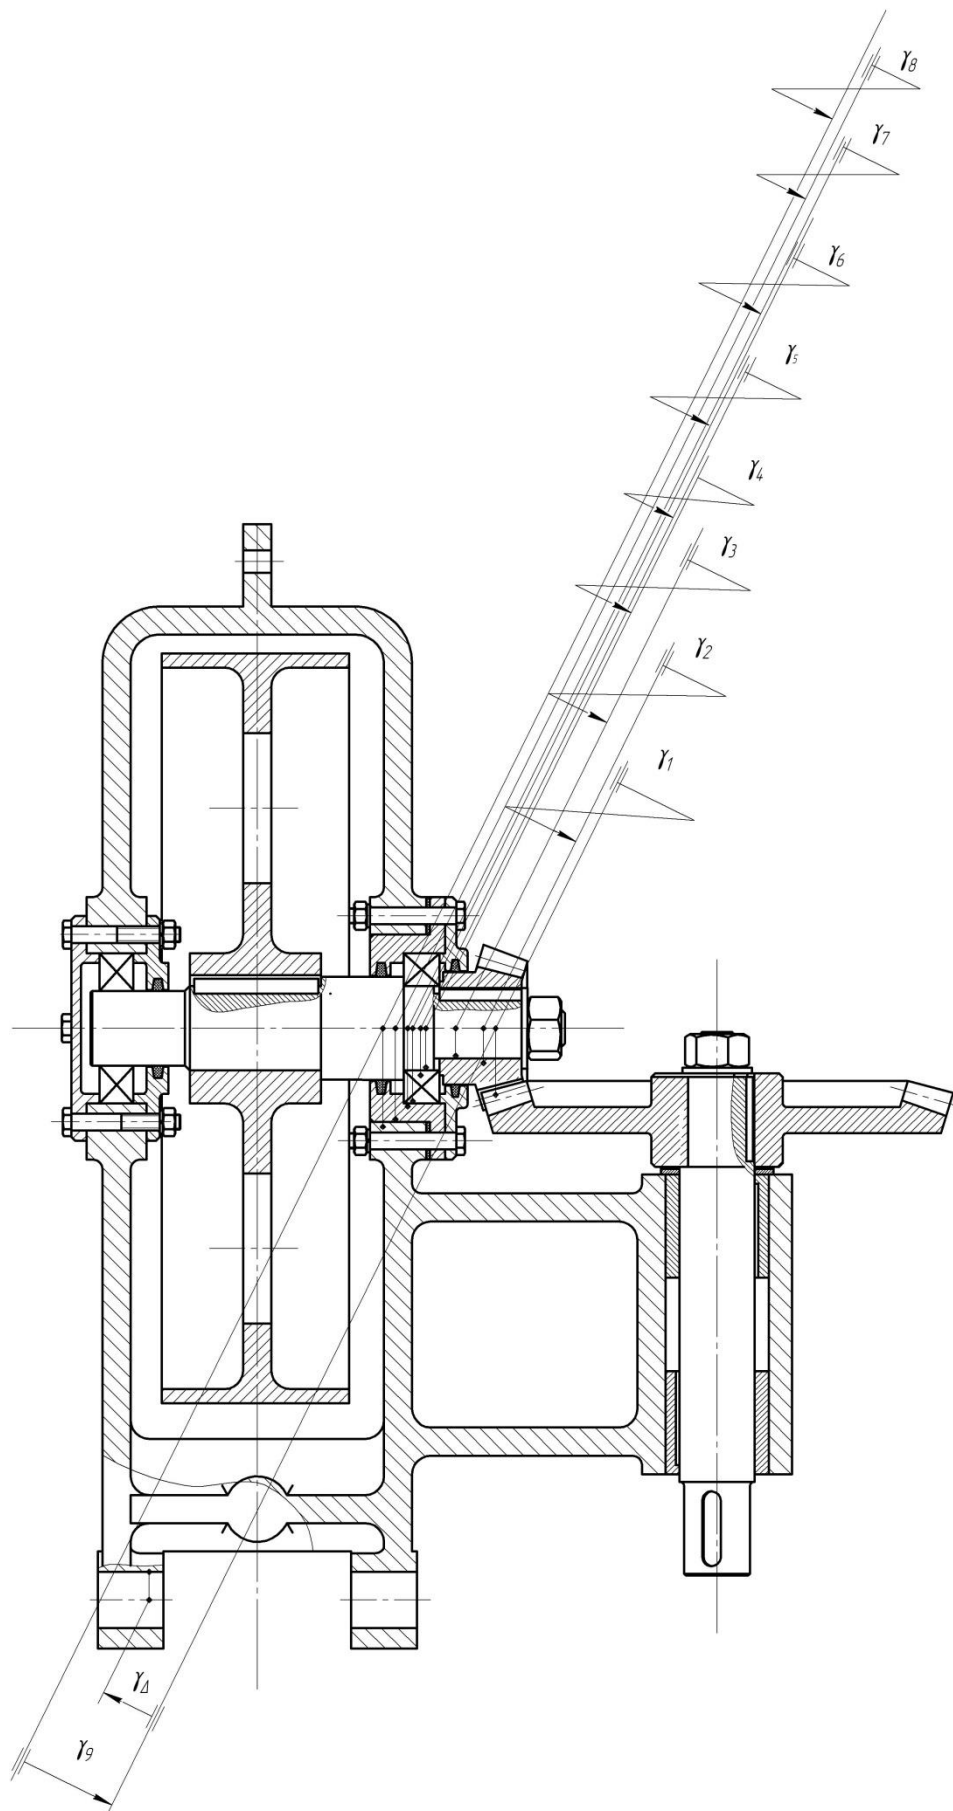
Розмірний ланцюг, який забезпечує точність кутового розташування зубчастих коліс
